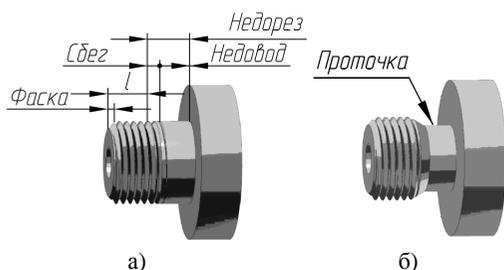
Элементы наружной цилиндрической резьбы без проточки (а) и с проточкой для выхода инструмента (б)
